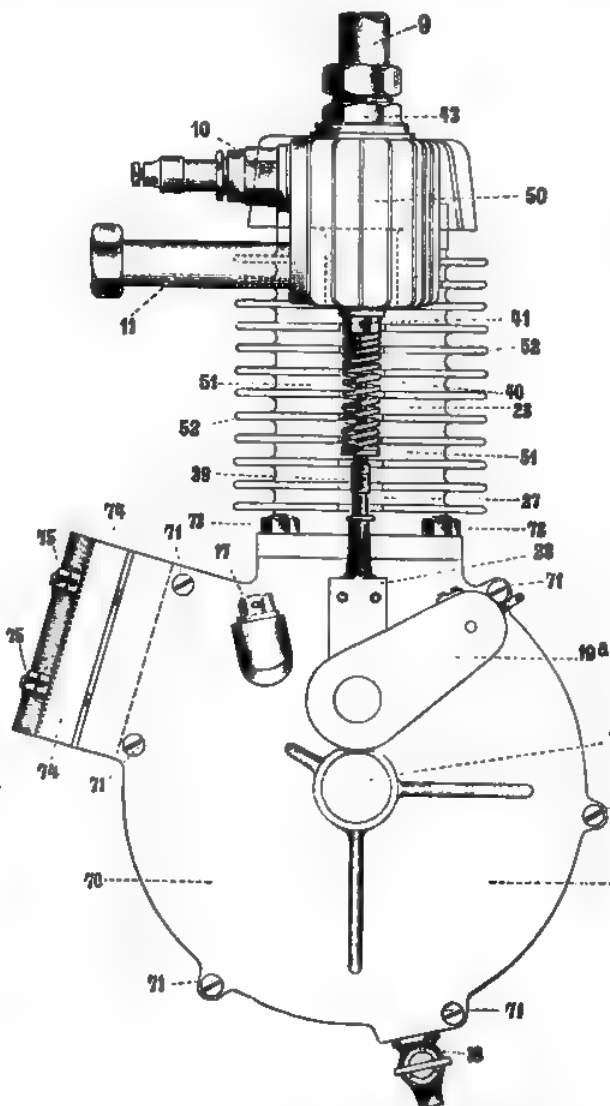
Rechte Seitenansicht des Z. L.-Motors.
